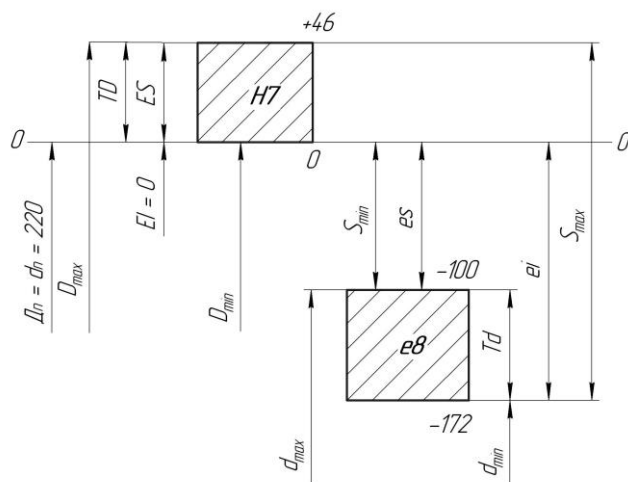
Схема полей допусков для посадки с зазором (пример)
